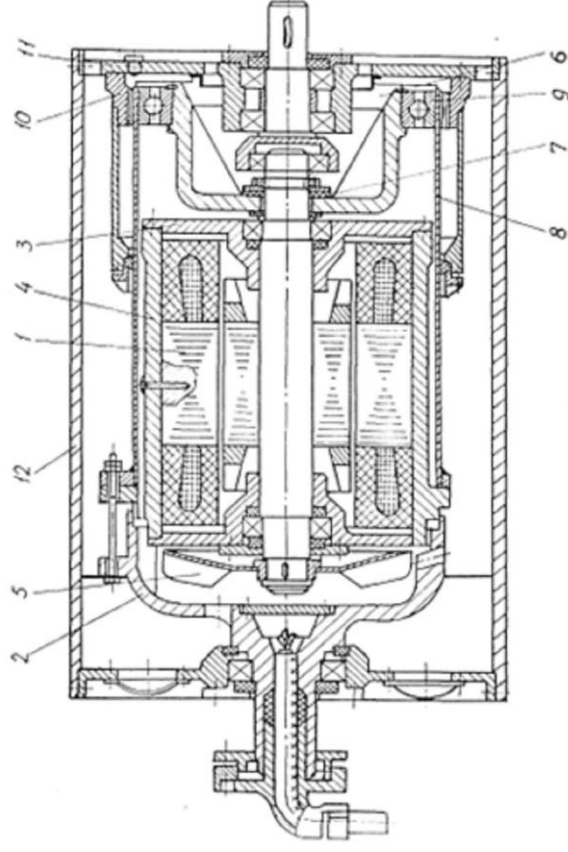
Вибухобезпечний електричний вмонтований привод з хвильовою передачею
